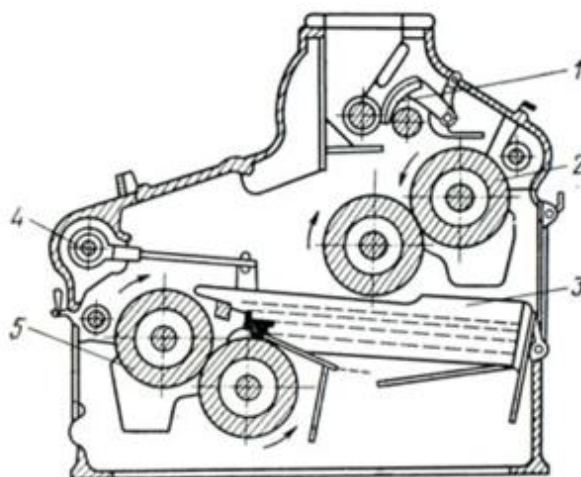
Чотирьох-валкова дробарка: 1 – транспортуєчий пристрій; 2 - верхня пара вальців; 3 - сита; 4 - привод до сит; 5 - нижня пара вальців [46]
